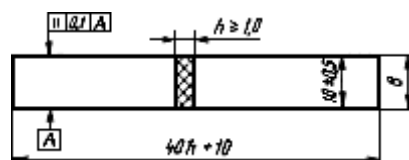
Креслення зразка у вигляді смуги прямокутного перерізу.
